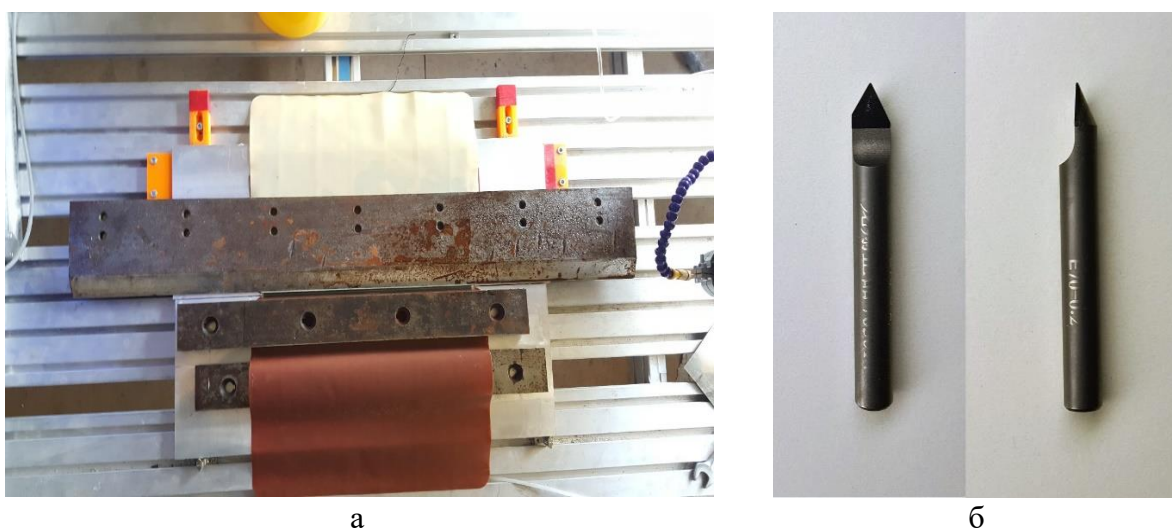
Обработка матрицы: а – крепление матрицы на столе станка с ЧПУ; б – алмазный конический гравер
